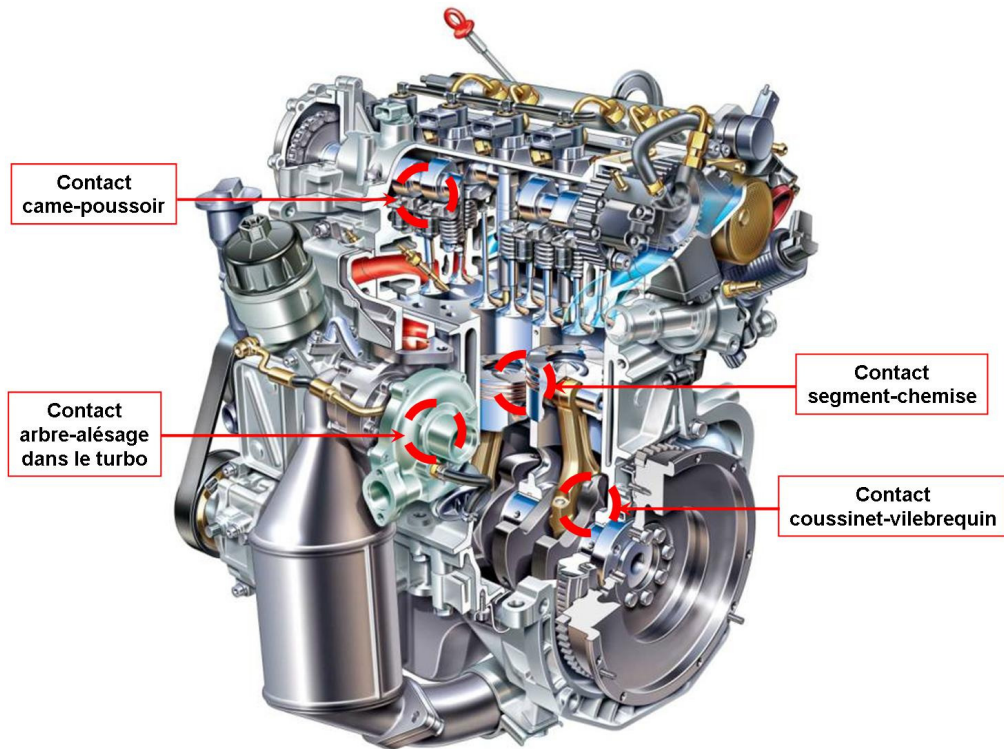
Vue éclatée d'un moteur thermique et illustrations de quelques zones de frottements.
